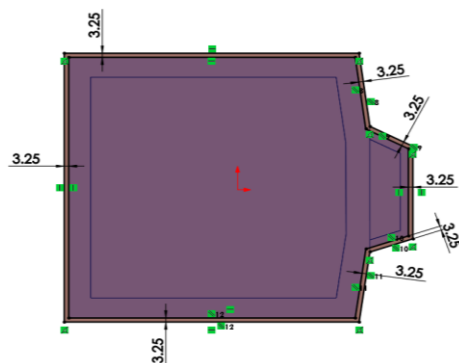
Trazado para realizar corte de paredes de la Superestructura
